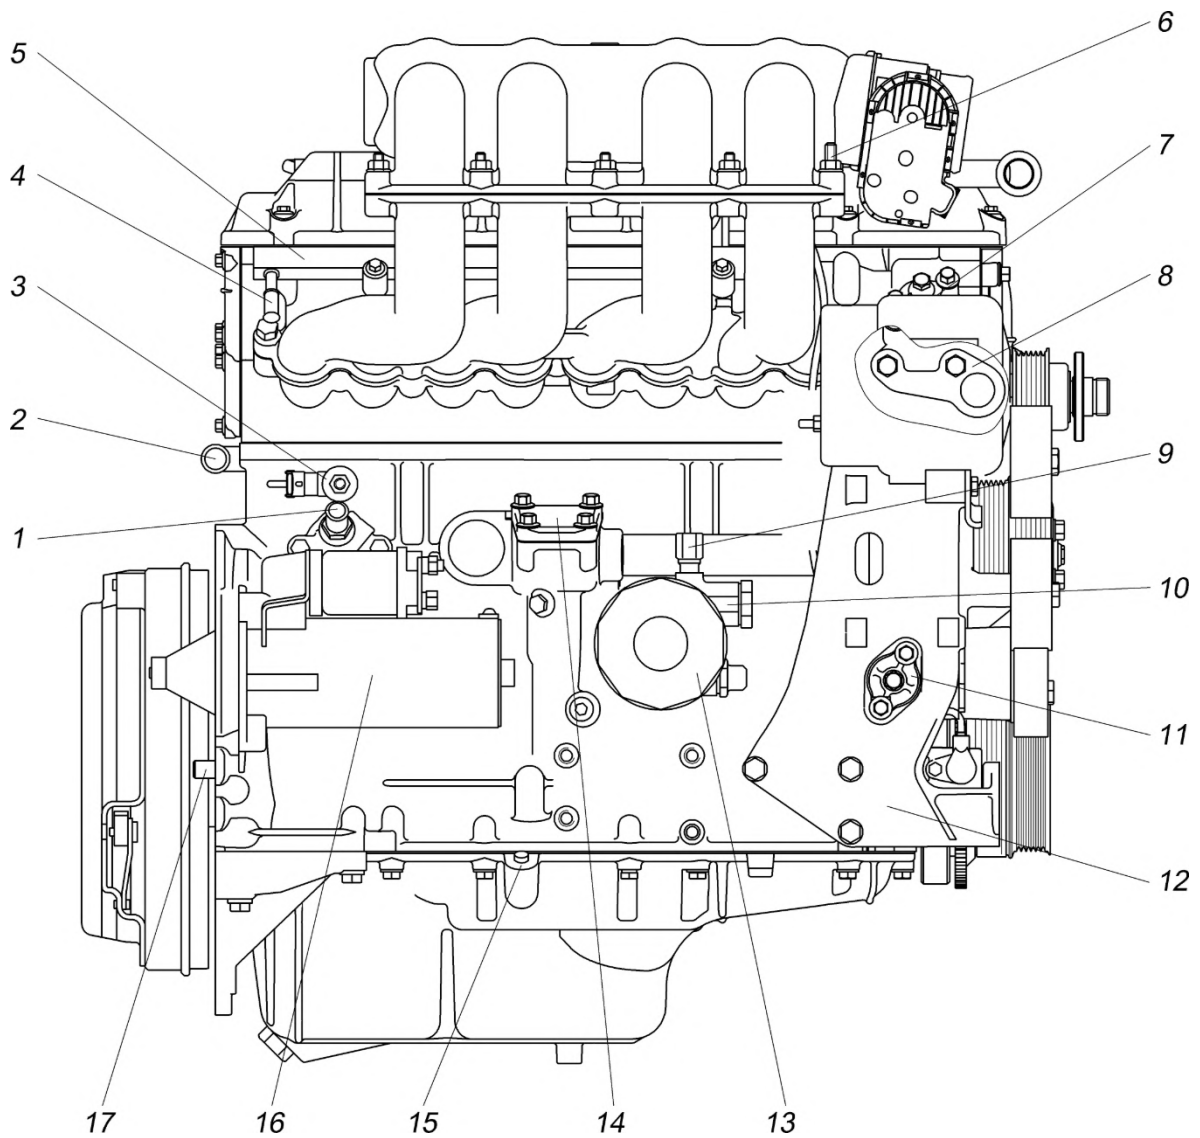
Ansicht des Motors ZMZ-40904.10 von links
